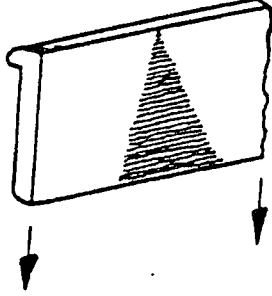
I profiline iki üfleçle ısı kaması ve ısı yolu uygulanması
